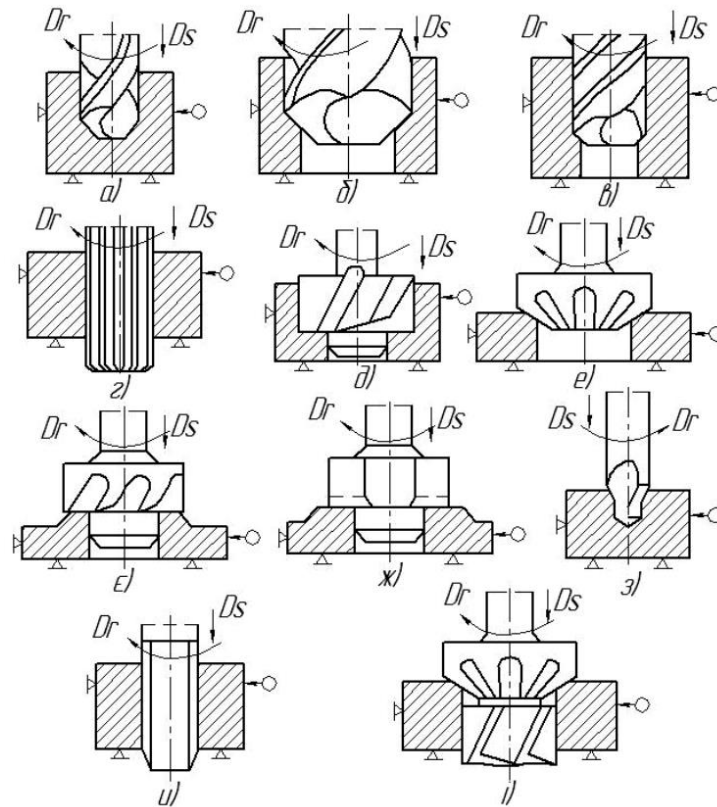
Схеми оброблення отворів на свердлильних верстатах:
